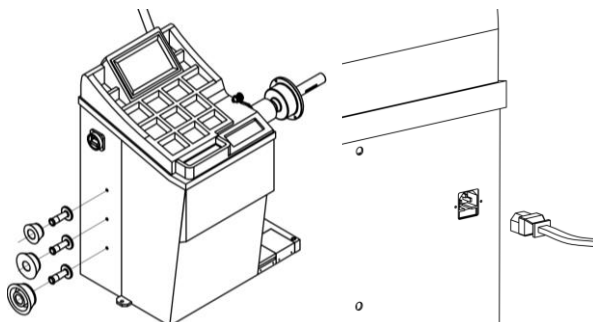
installazione manicotto dell'asta Fig.9 potenza di collegamento
